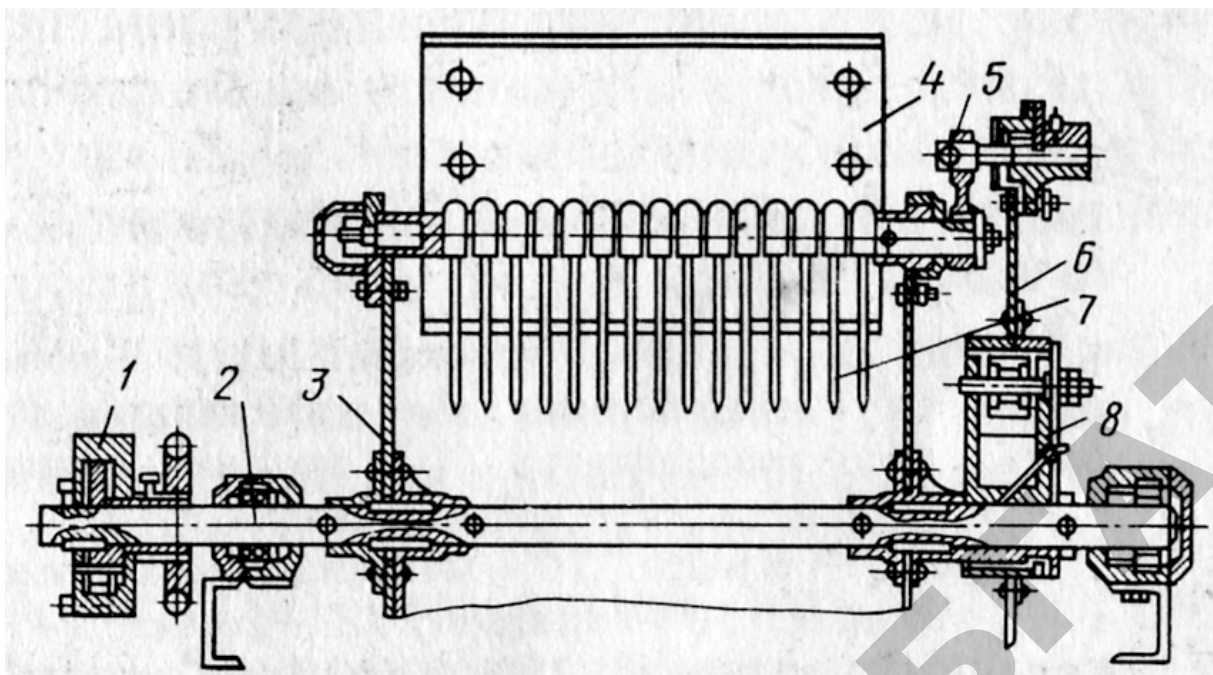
Очесывающий барабан льноуборочного комбайна ЛК-4А:
